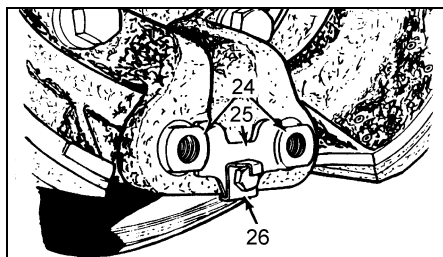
24 - анкерный палец, 25 - стопорная пластина, 26 - стопорная пластина.
